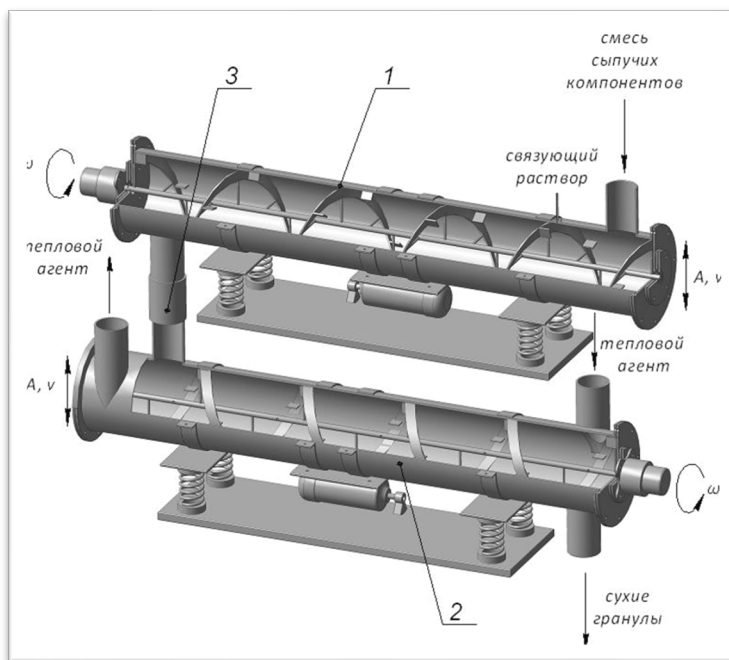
Барабанный виброагрегат: 1 – барабанный виброгранулятор; 2 – барабанный виброкатыватель-сушилка; 3 – эластичный рукав
